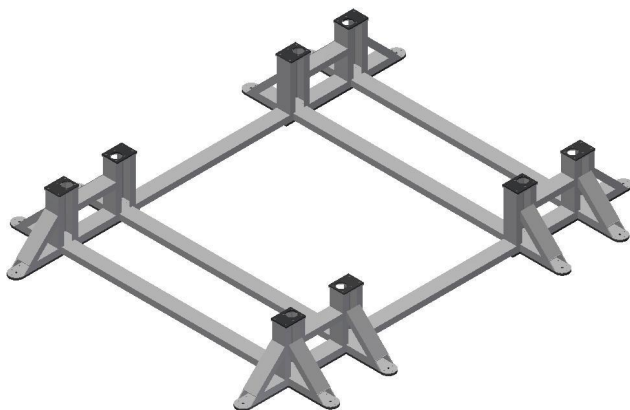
Общий вид стенда для испытания тележек типа 68-797, 81-717 и 81-714 вагонов метрополитена
